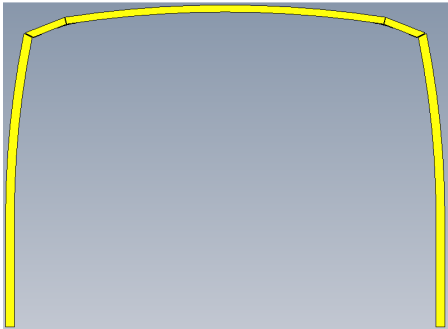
Pórtico de rigidez transversal: Conjunto completo Pilar+Arco tejadilho
